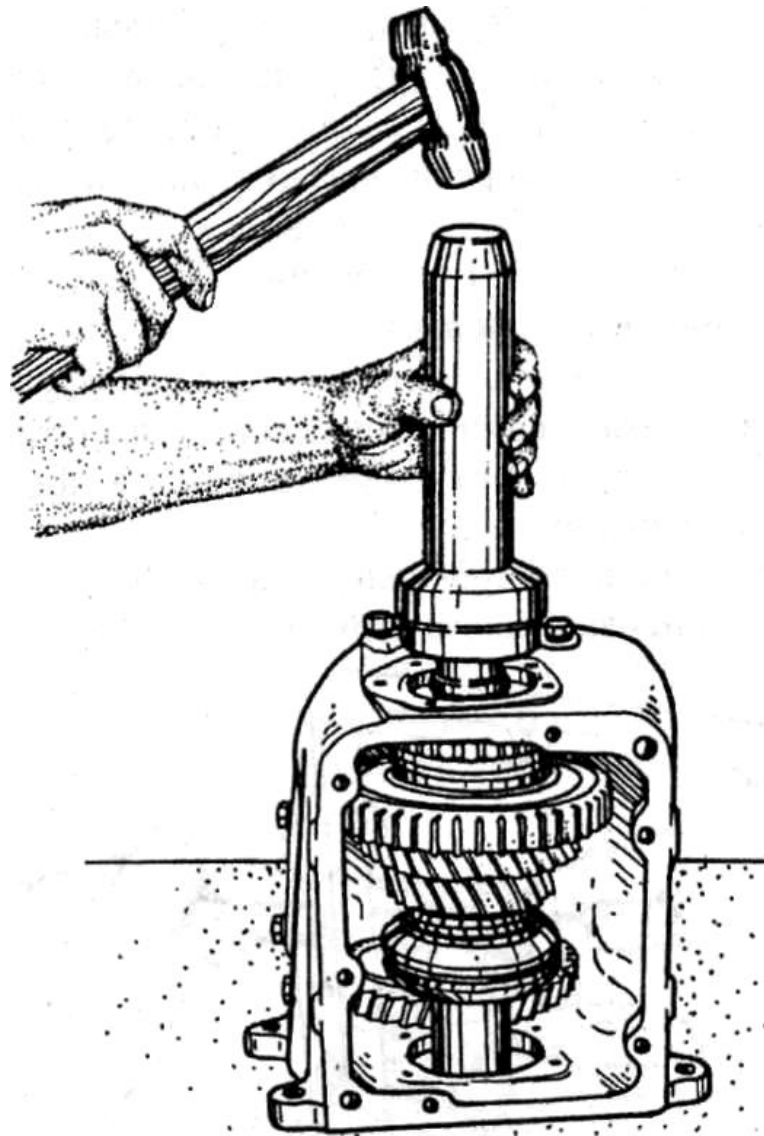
Напресування кулькового підшипника вторинного вала
